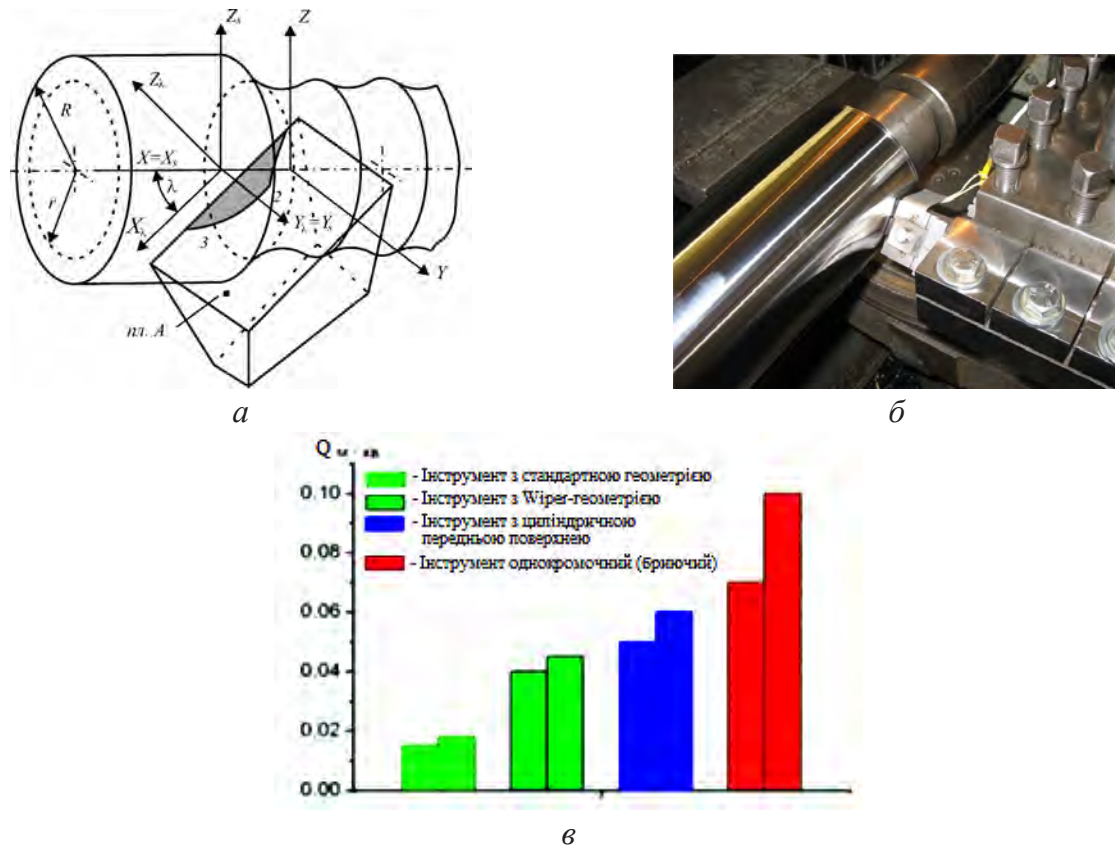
Схематичне зображення знімасого припуску при «бриучому» обробленні (а), оброблення деталі із загартованої сталі «бриучим» різцем (б) поверхнева продуктивність оброблення інструментами, оснащеними ПКНБ, забезпечуючим шорсткість обробленої поверхні  $Ra$  0,32...0,63;  $Rz$  1,5...5,0 (в)
